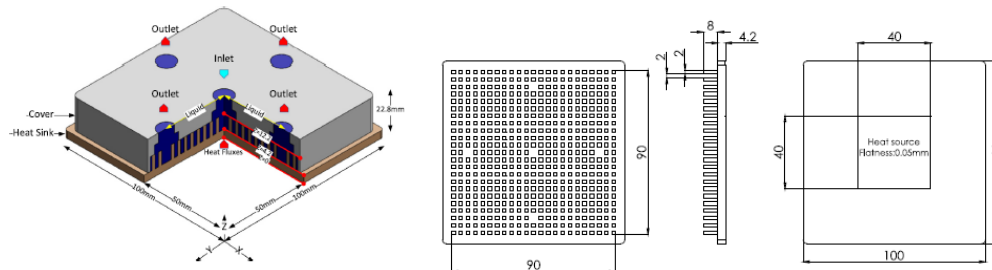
Dimensiones del disipador de calor con minialetas [27].
